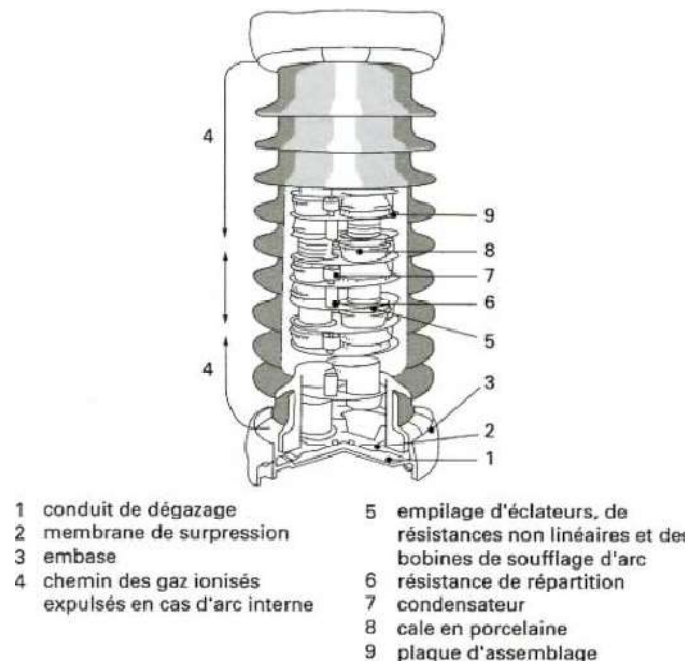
Parafoudre au carbure de silicium et à éclateur [9]
